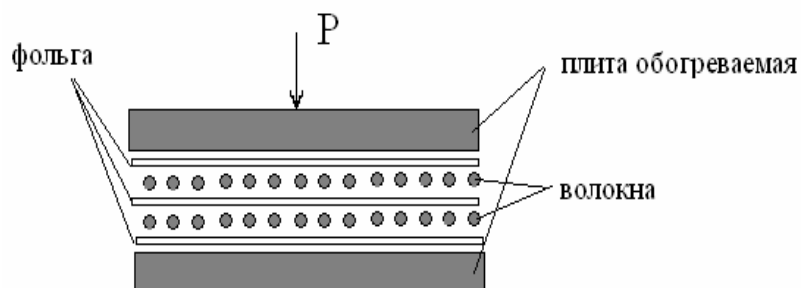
Схема получения КМ диффузионной сваркой
